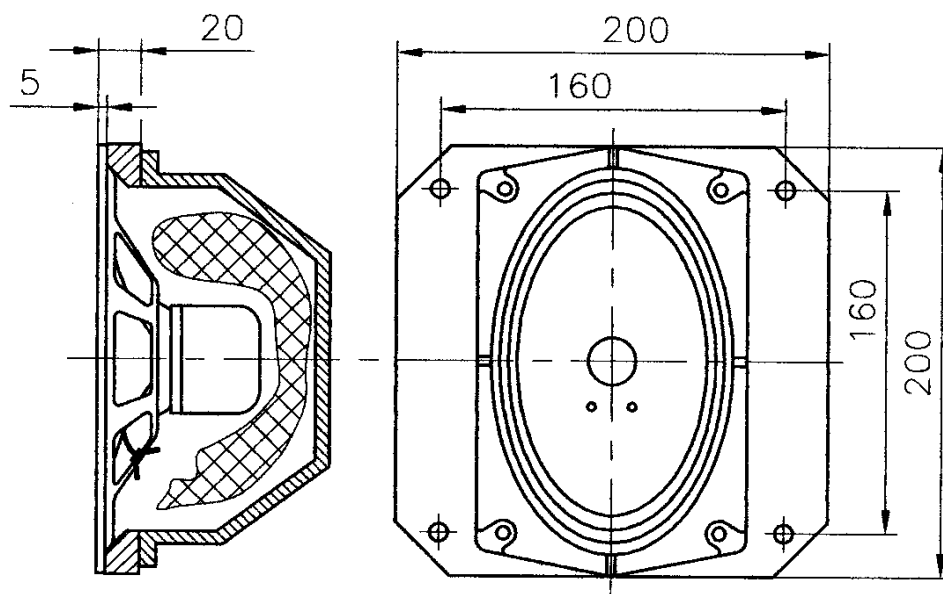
Внешний вид фланца-переходника, для установки динамика 3ГД-32.
